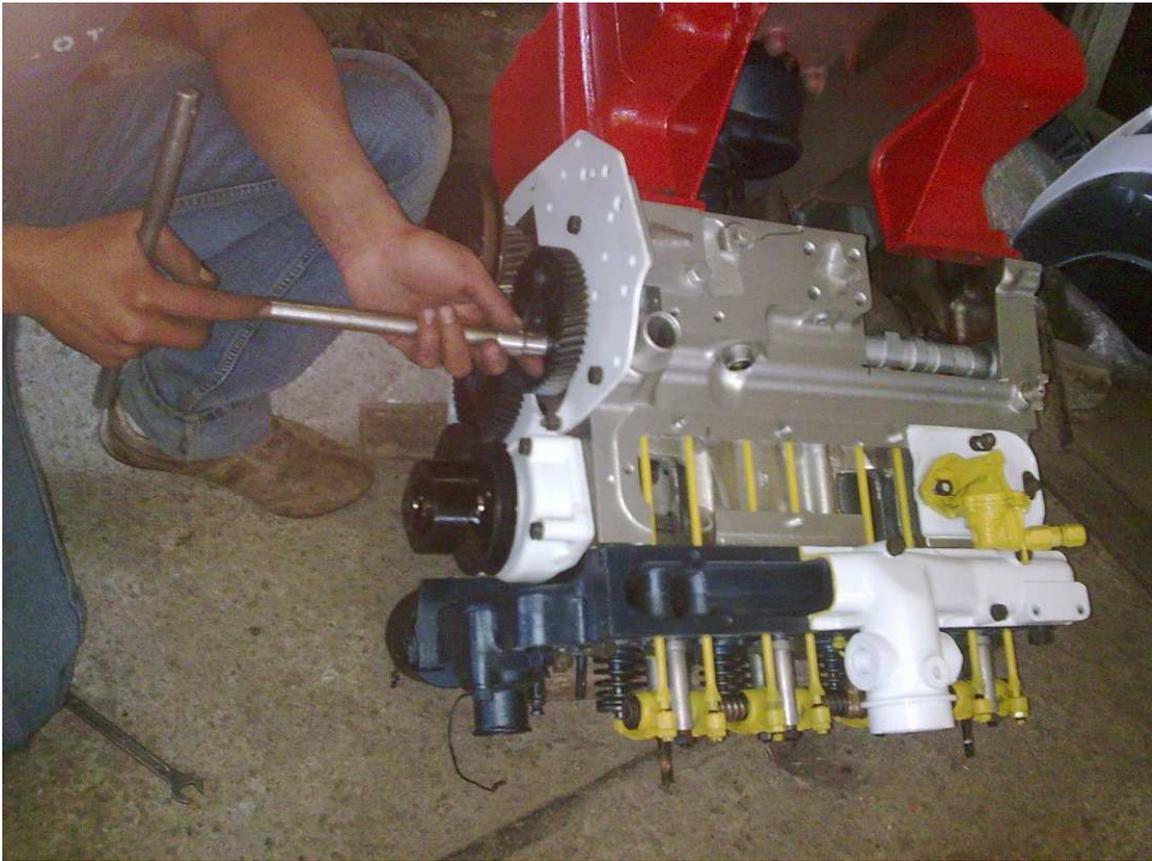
Montaje de los engranajes de sincronización y poleas
